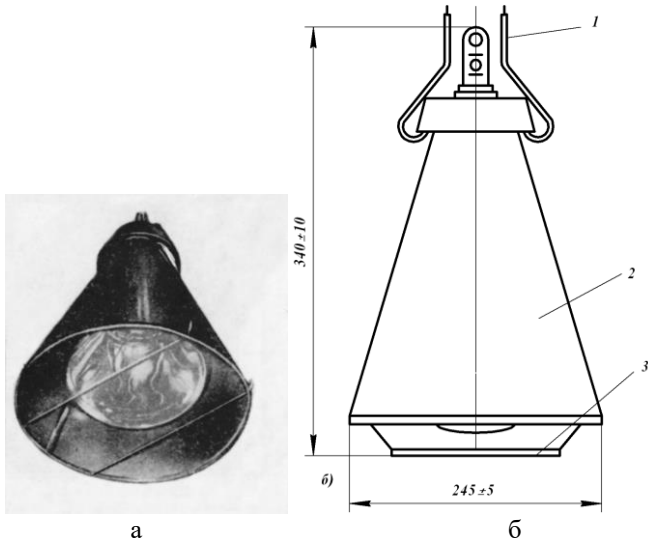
Інфрачервоний опромінювач типу ОРИ-1: а) загальний вигляд; б) схема конструкції: 1 – підвіска; 2 – корпус; 3 – сітка
